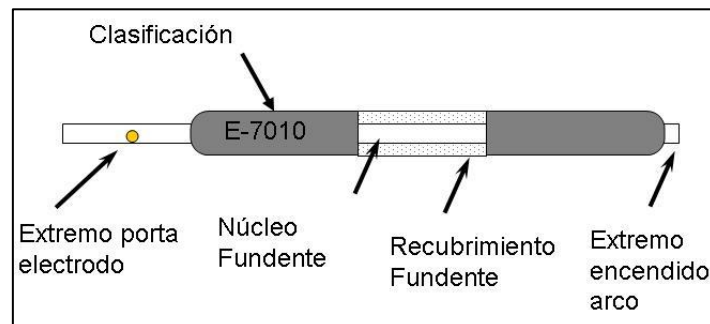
Componentes de un electrodo para la soldadura SMAW.
